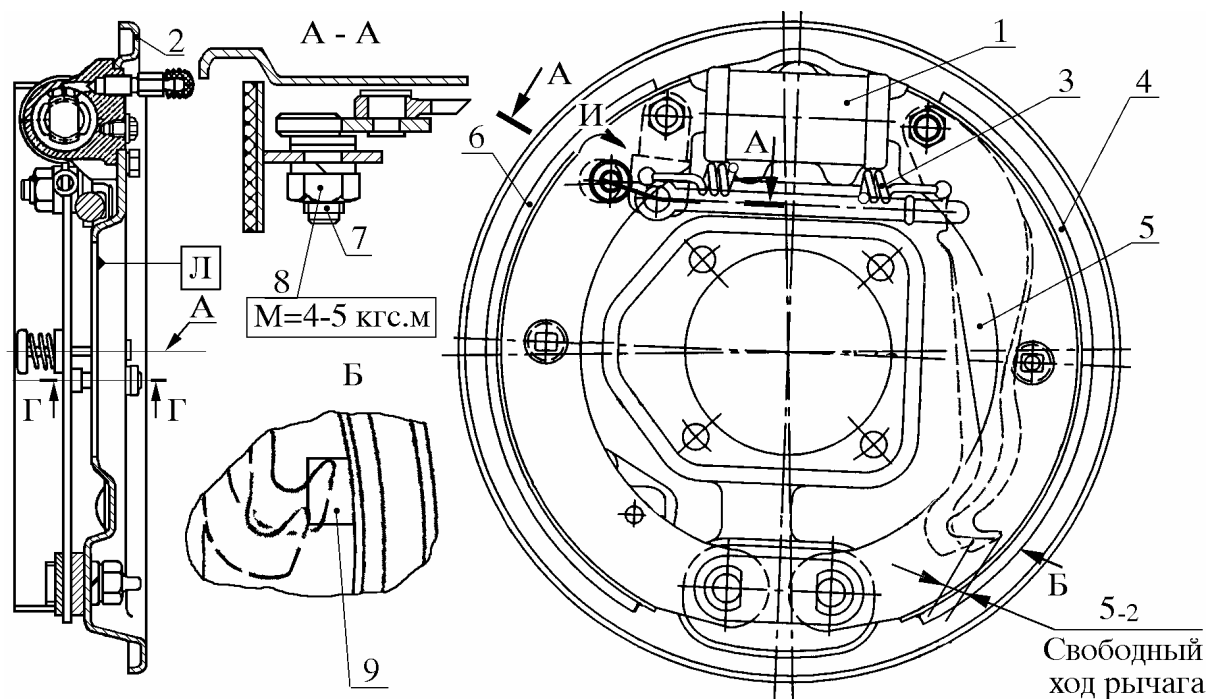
Установка стяжной пружины и регулировка свободного хода приводного рычага:
